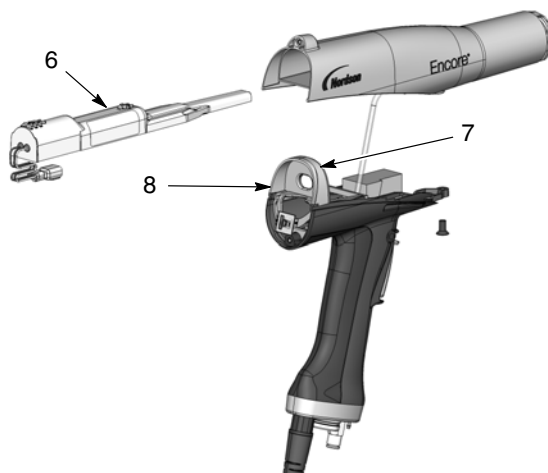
Demontáž tělesa pistole z rukojeti
